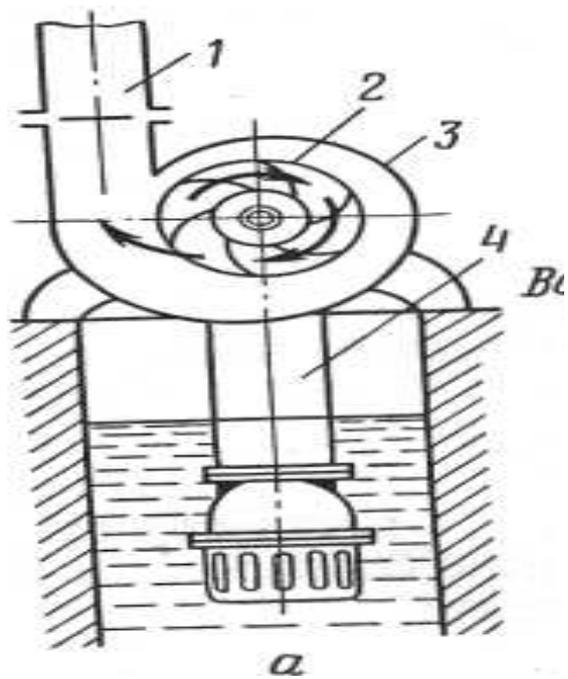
Центробежный насос: 1 — напорный патрубок; 2 — рабочее колесо; 3 — корпус; 4 — всасывающий патрубок.
